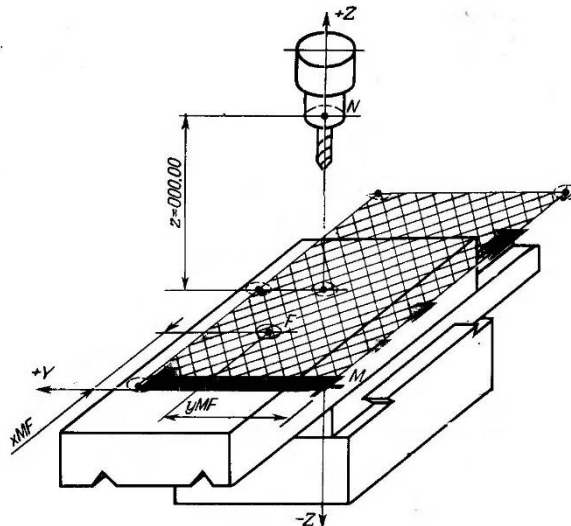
Система координат свердлувального або фрезерного верстата
